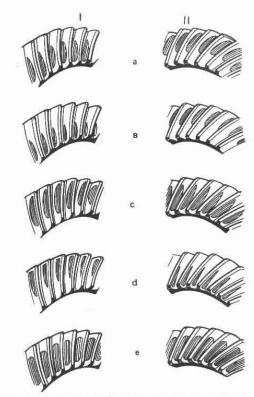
Disposición de la huella de contacto en el engrane de los piñones de ataque y conducido del engranaje de ángulo:
